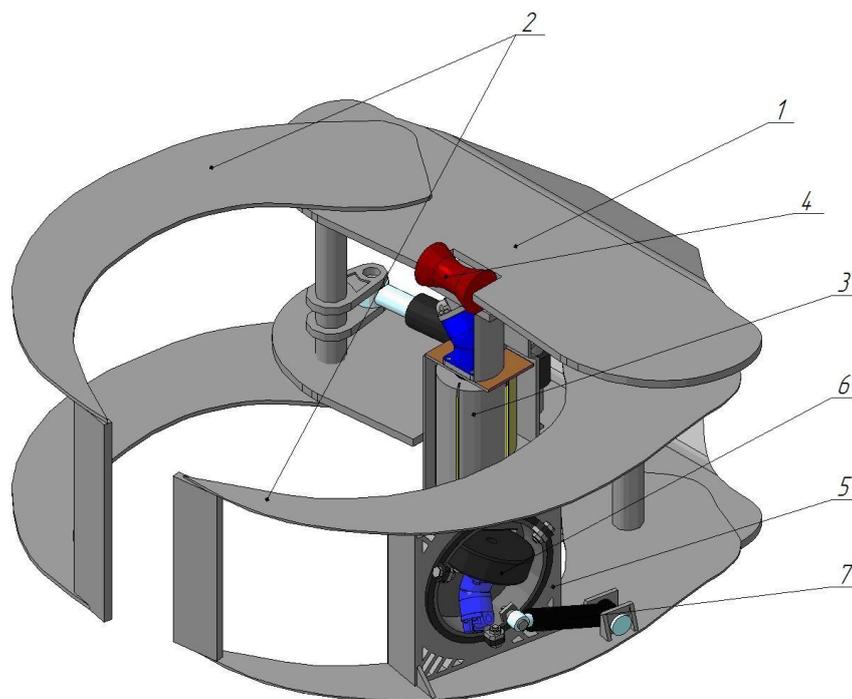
Схема модернизированного грейферного захвата: 1 – корпус; 2 – внутренний и наружный захват; 3 – фреза с приводом; 4 – опорный направляющий валец; 5 – площадка для привода подачи бревна; 6 – гидромотор привода подачи бревна; 7 – гидроцилиндр поворота привода.
